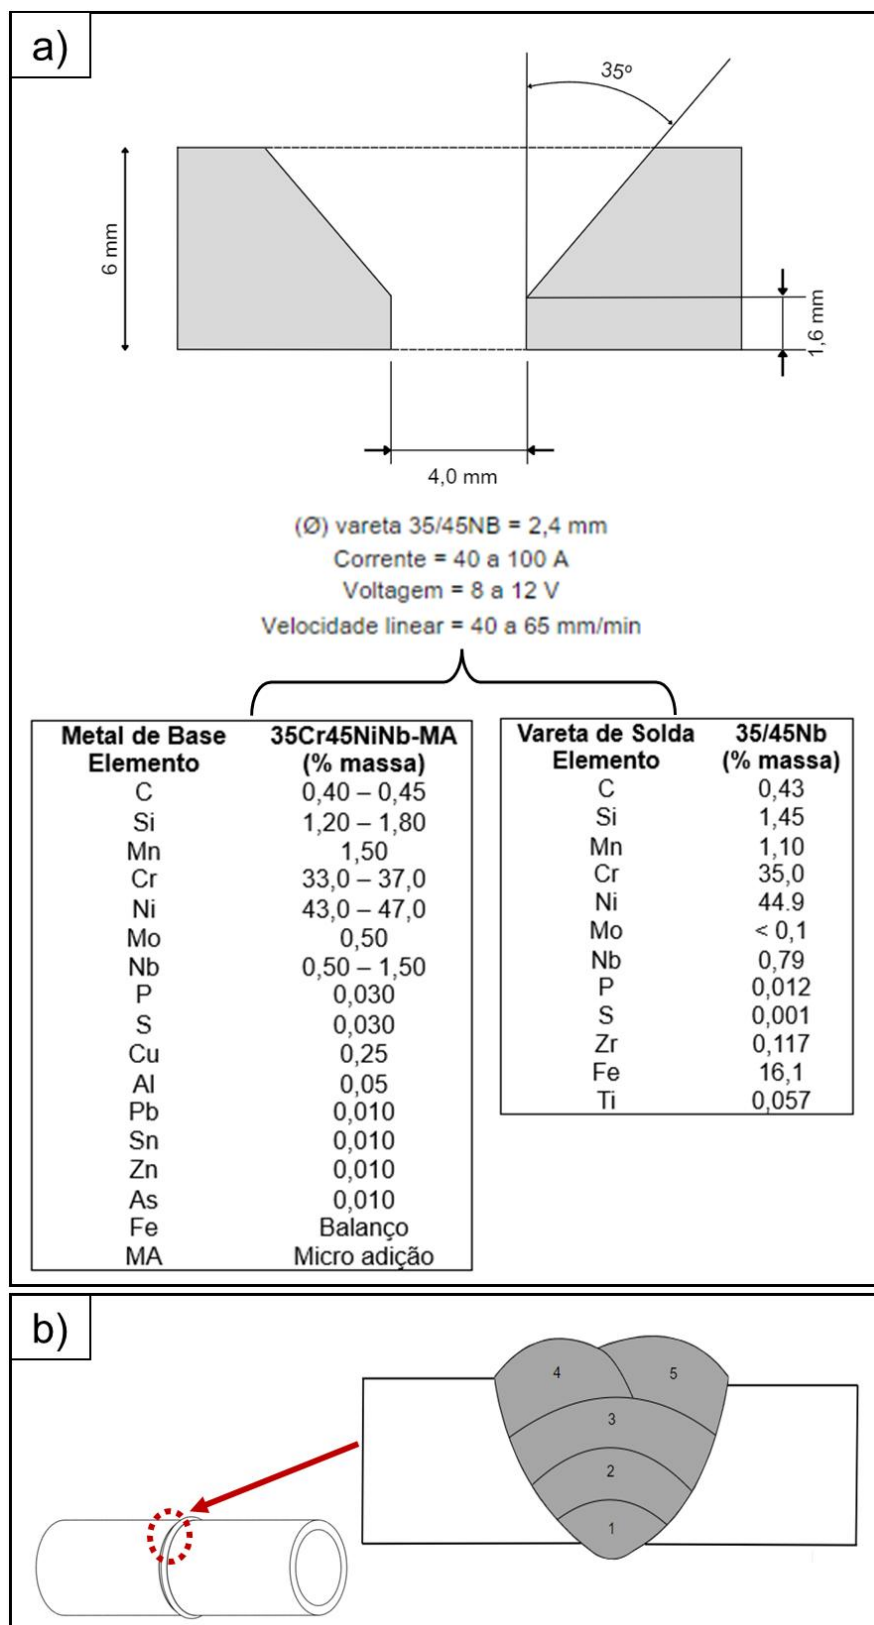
(a) Esboço dos chanfros de solda, parâmetros, metal de base, vareta de solda e (b) a sequência de passes empregada na soldagem das amostras.
